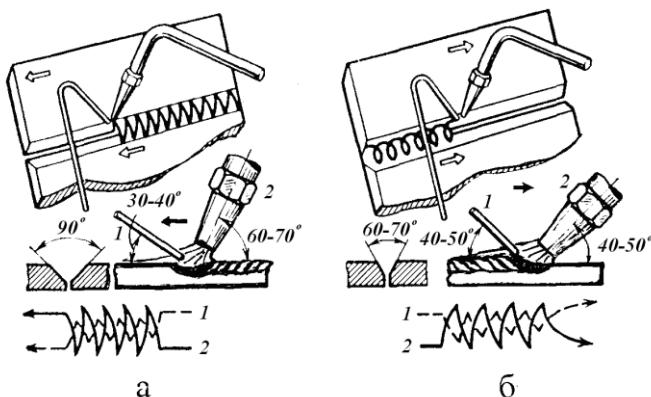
Способы сварки – левый (а) и правый (б): 1 – присадочный металл; 2 – горелка (стрелками показано направление сварки)
